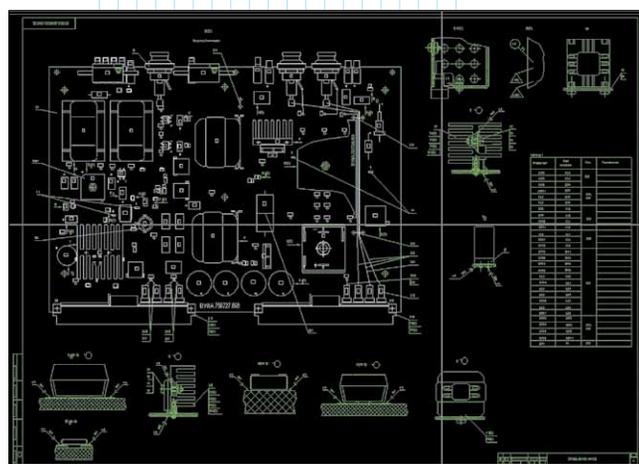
Размещение чертежей установки (вариант 1) компонентов на листе 1 сборочного чертежа печатной платы (слой TOP Silk – белый цвет, TOP Assy – зеленый)
